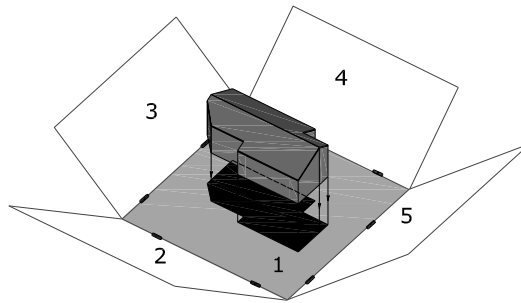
Rabattement des plans verticaux dans le prolongement du plan horizontal (vue de dessus)
